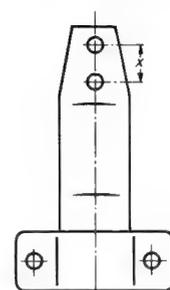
Haltefuß E; Eisenblech, 3 mm stark, verzinkt oder wetterfest lackiert
